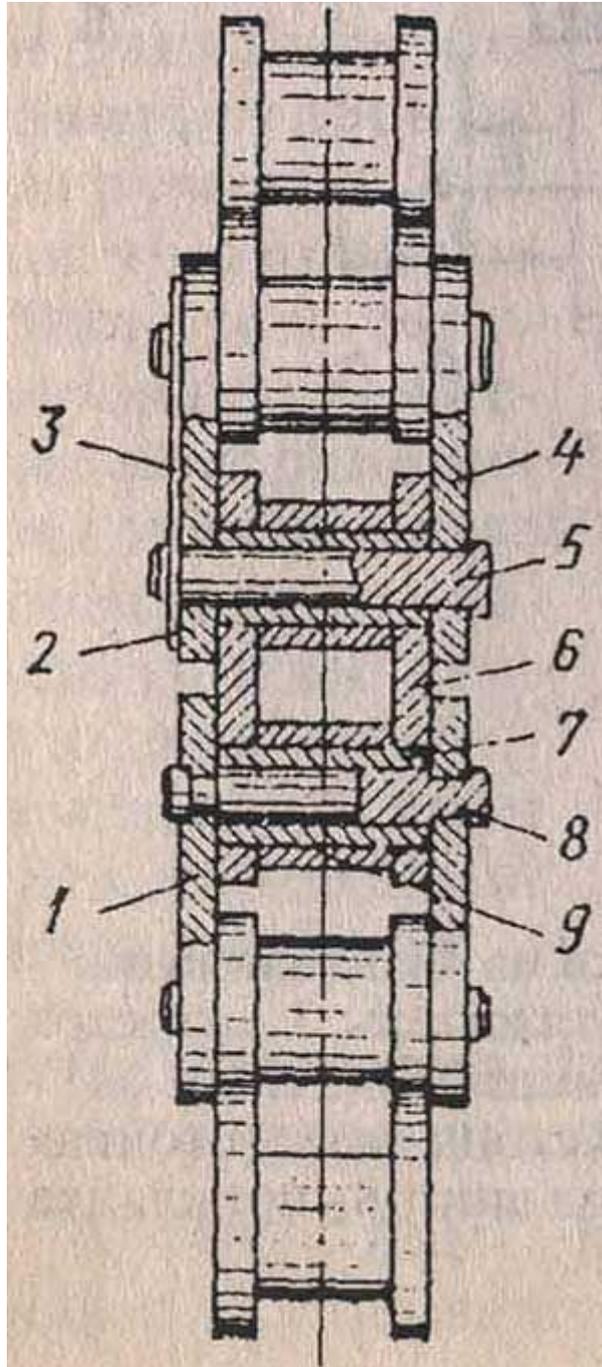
Разрез цепи задней передачи: 1 и 6 - пластины; 2 - съемная пластина замкового звена; 3 - пружинная защелка замкового звена; 4 - замковое звено; 5 - валик замкового звена; 7 - втулка; 8 - валик; 9 - ролик металлической крышки 2. Крышка удерживается на кожухе пластинчатой пружиной 3.
